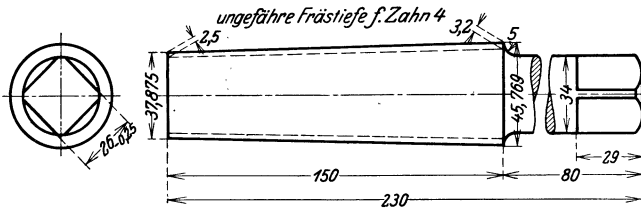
Werkzeugzeichnung zu einer Reibahle.
